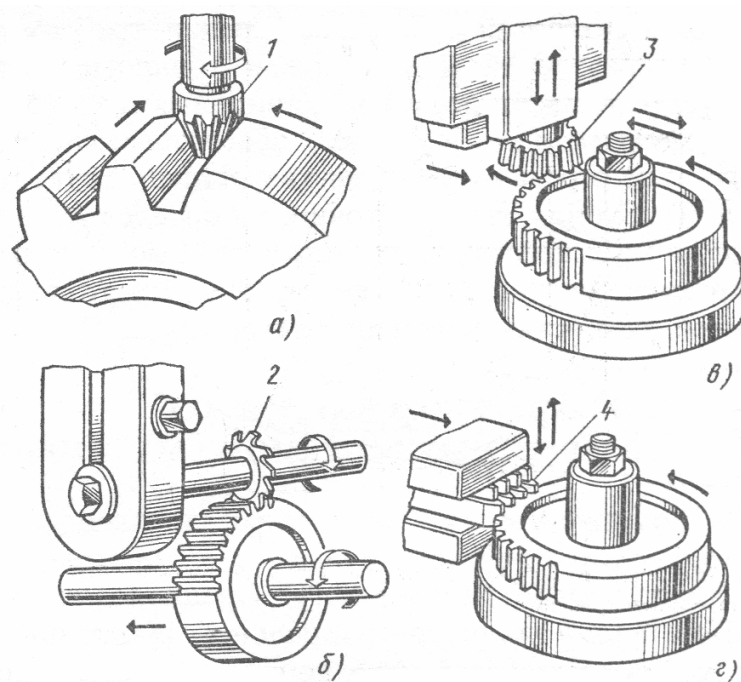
Нарезание зубчатых колес копированием с помощью фрез и обкаткой с помощью долбяка и гребенки: 1 – пальцевая фреза; 2 – модульная дисковая фреза; 3 – долбяк; 4 – гребенка
